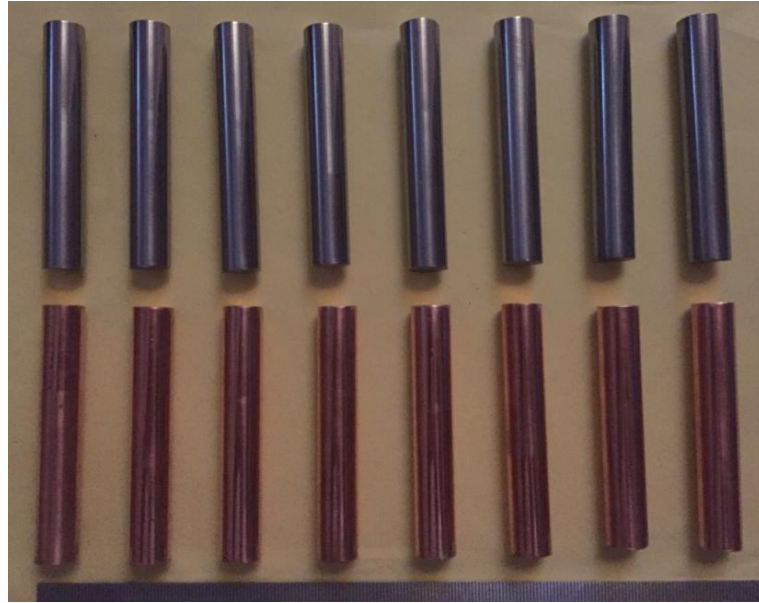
Pièces AISI 316L et Cuivre à souder par friction rotative.
